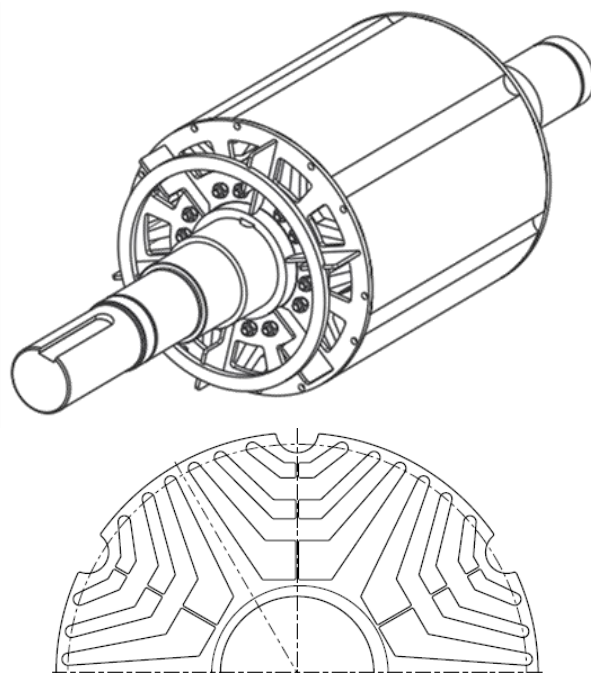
Общий вид ротора ТЛА конструкции синхронно-реактивного двигателя и вид $\frac{1}{2}$ листа ротора
